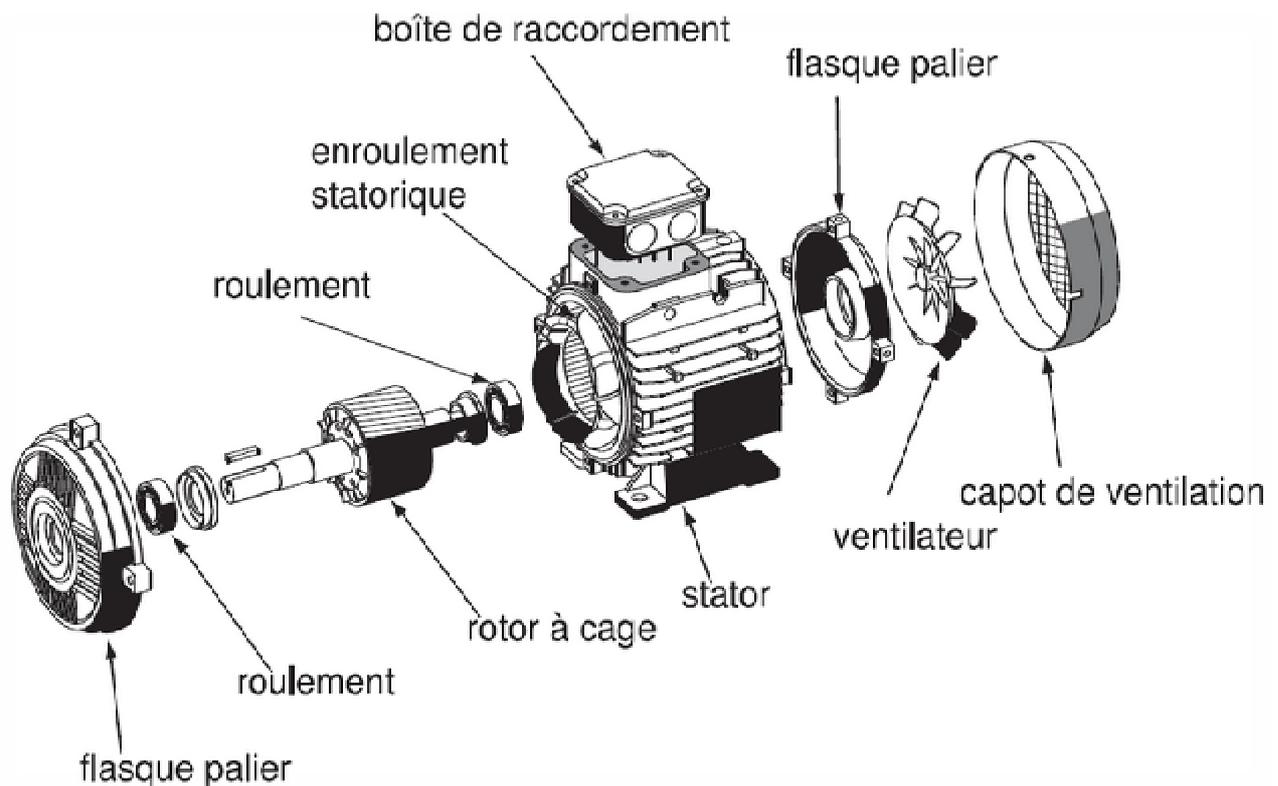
Vue éclatée d'un moteur asynchrone à cage d'écureuil moulée.
